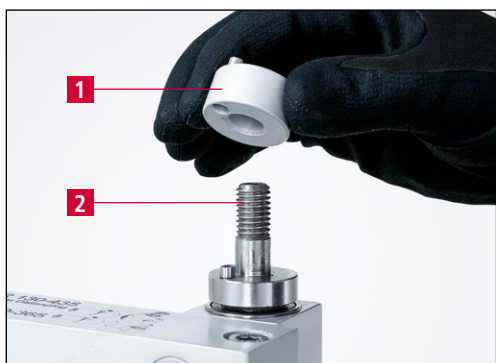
Установка регулировочной шайбы на болт крепления
